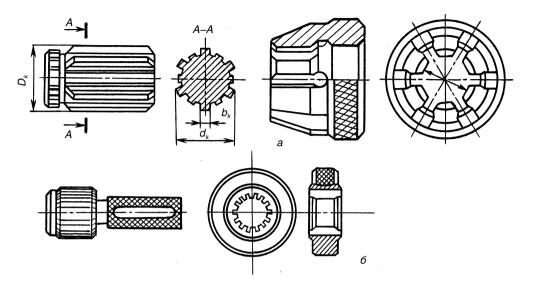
Комплексные шлицевые калибры для контроля элементов шлицевых соединений: а — прямобочных; б — эвольвентных
